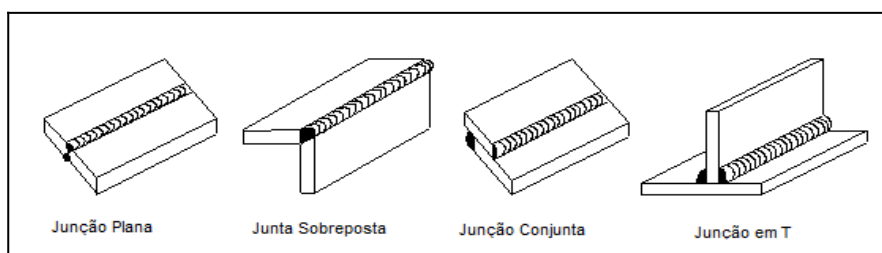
Tipos de junta na soldagem eletrodo revestido
